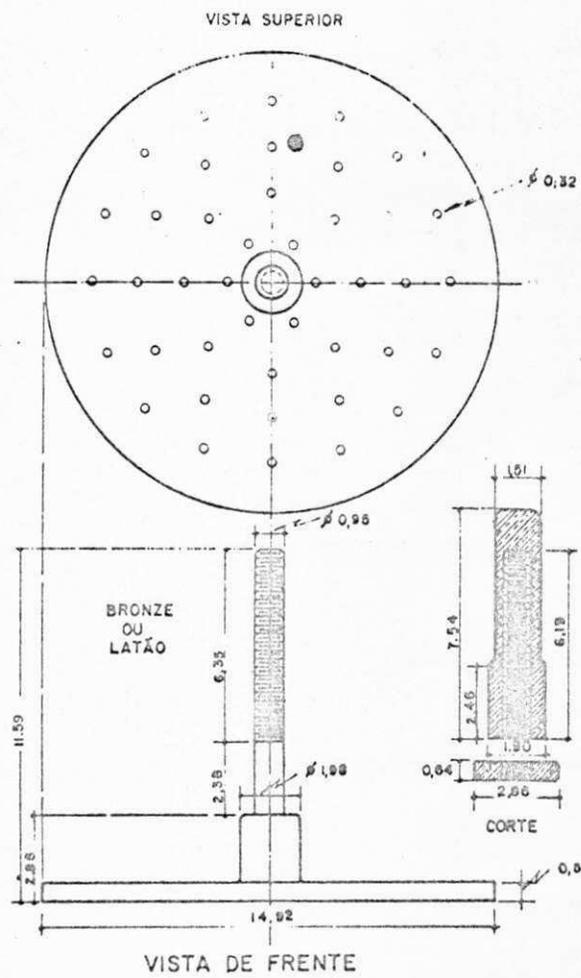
PRATO PERFORADO COM HASTE AJUSTÁVEL
